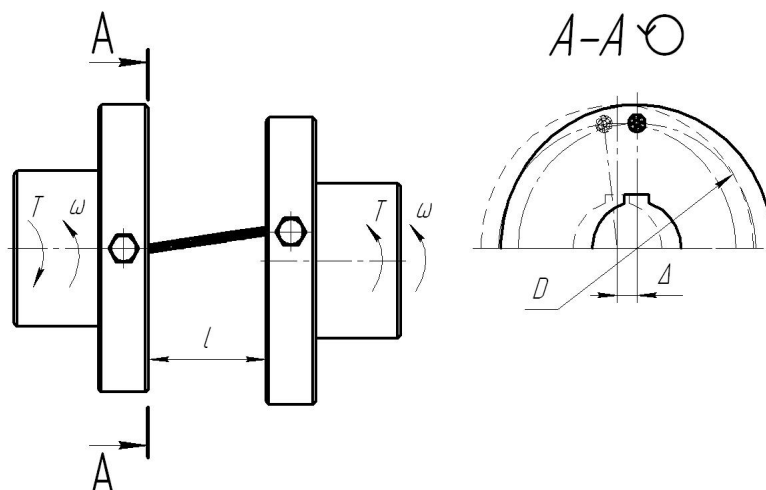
Схема муфти з осью паралельною установкою канатів прямолинійної форми
